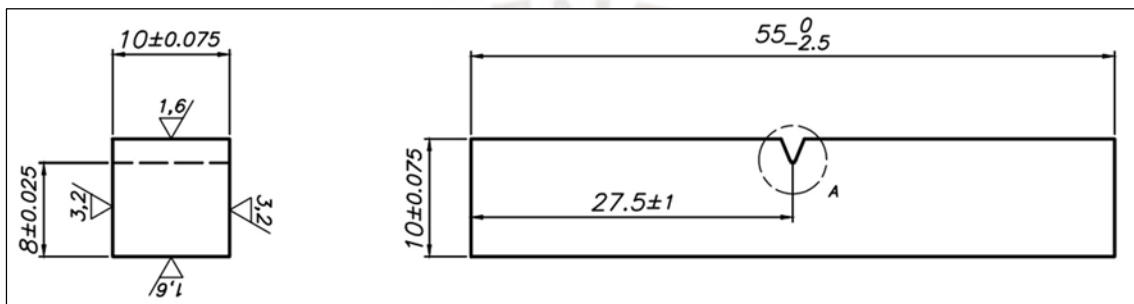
Plano de probeta para ensayo de impacto Charpy "V" Notch
